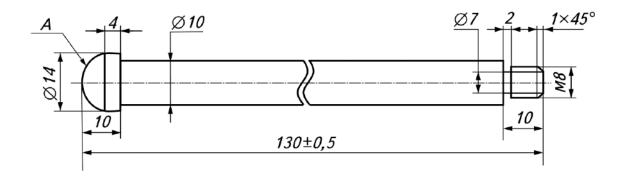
Рукоятка для винтового зажима столярного верстака
